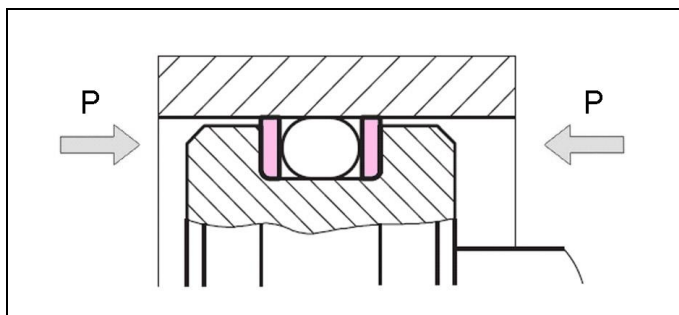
Installazione dell'anello di supporto, direzione di pressione sui due lati
